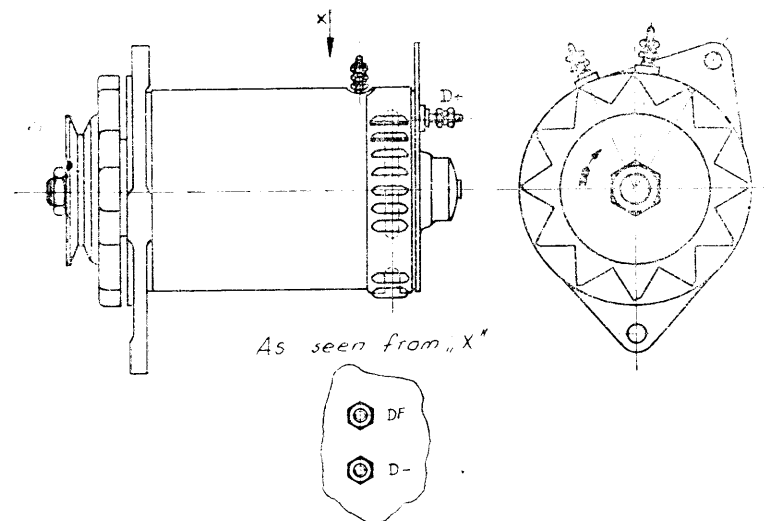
Gleichstromlichtmaschine — G-450-1.
